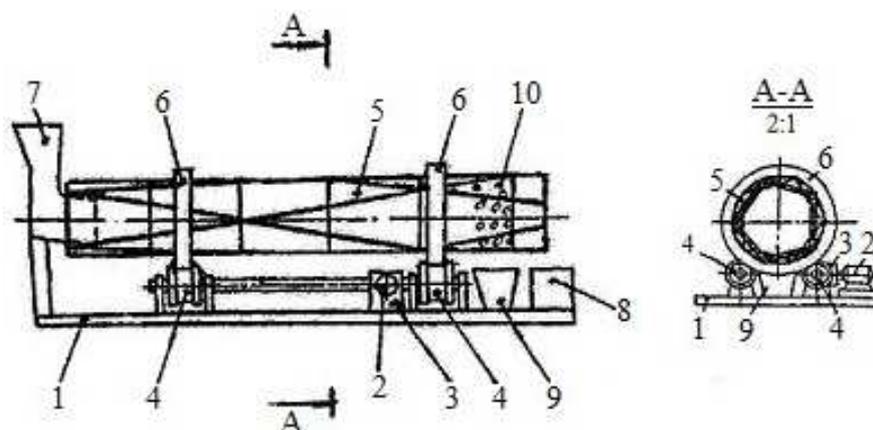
Схема станка для отделочно-зачистной и упрочняющей обработки деталей машин на базе релятивных винтовых барабанов
